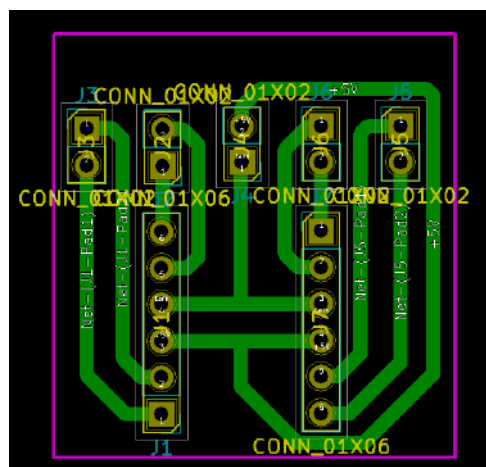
PCB do circuito eletrônico para acoplamento dos cabos dos motores.
